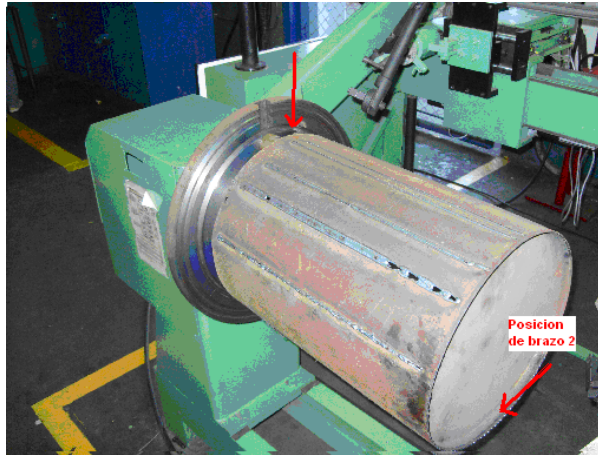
Posición del brazo 2 para comienzo de la soldadura del fondo del tanque
